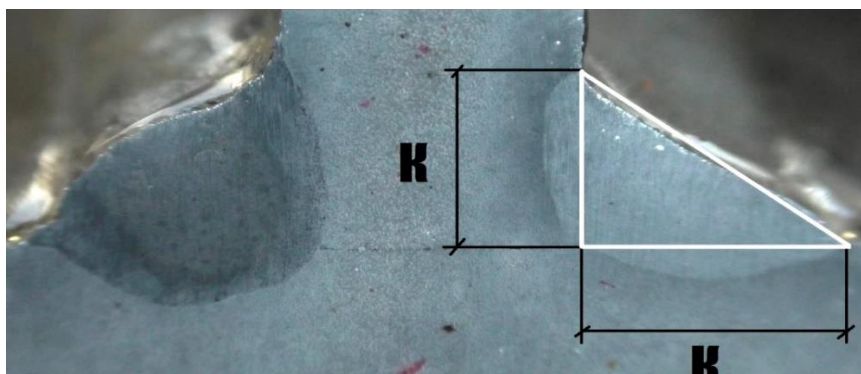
Поперечний розріз таврового зварного з'єднання
